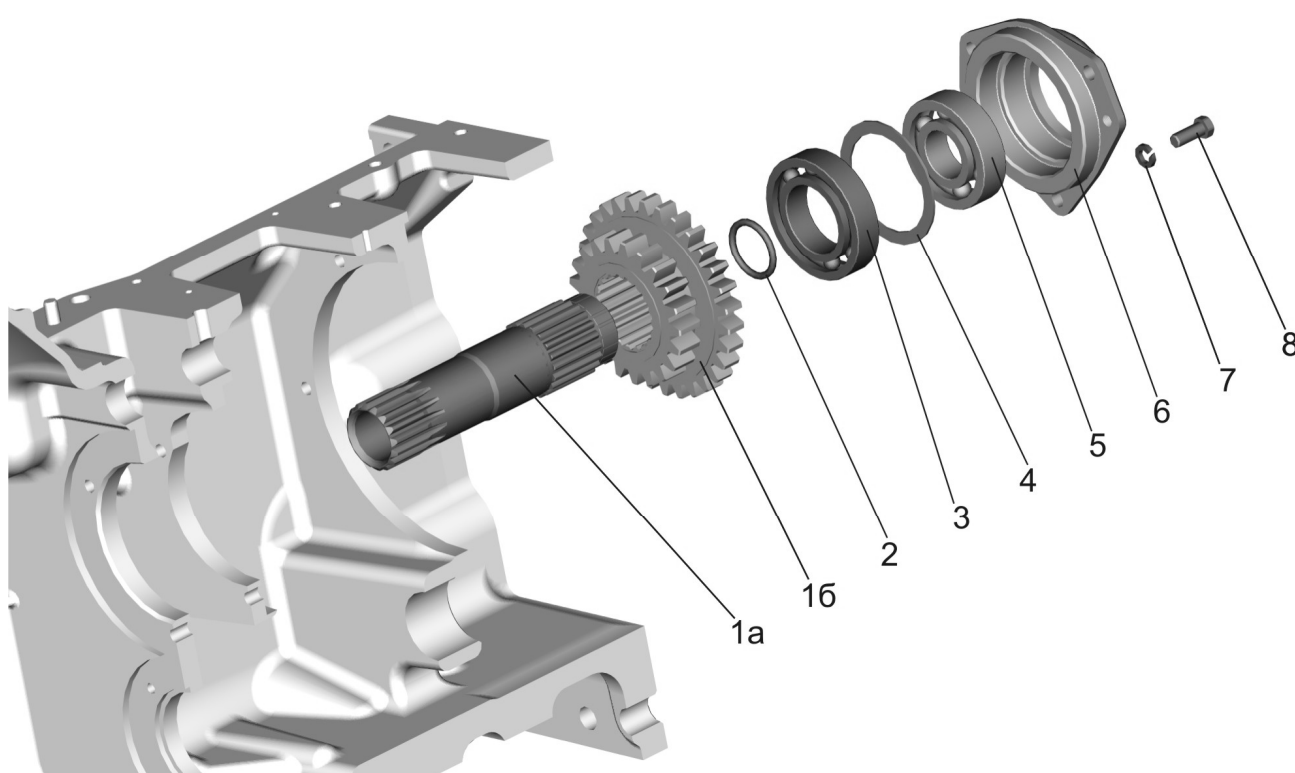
Корпус сцепления. Привод ВОМ. ($n_{\text{дв}}=1800$ об/мин)
